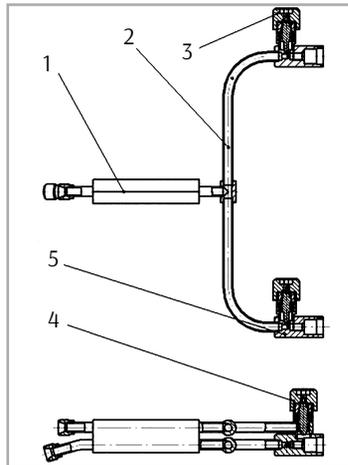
Ствол горелки для нагрева рельсов ГЗУ6-ЖД
